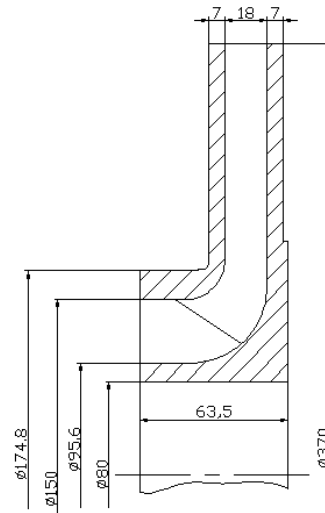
Эскиз исходного рабочего колеса с  $D_2=370$  мм
